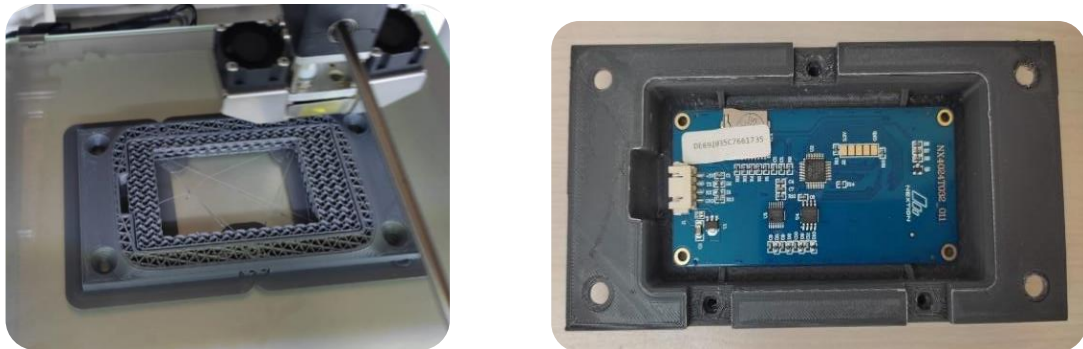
Impresión modelo final para cubierta frontal. Fuente: Autor
